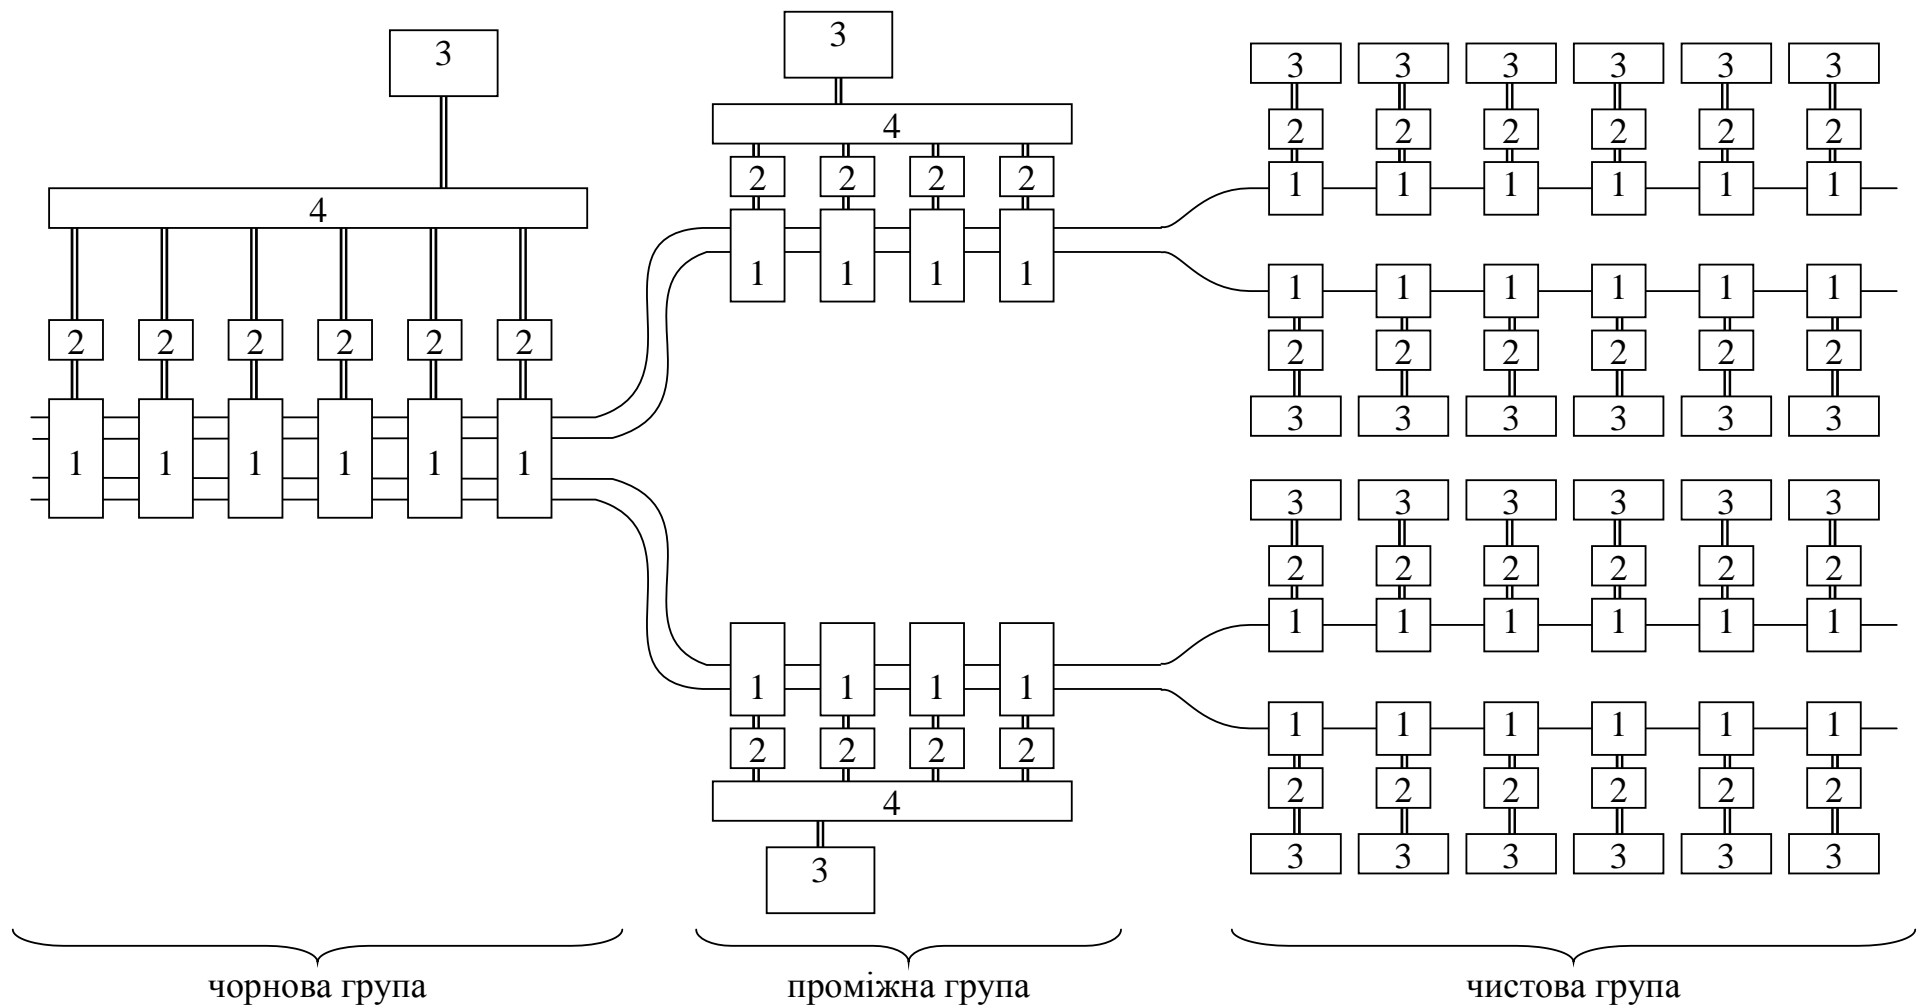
Схема розташування обладнання неперервного дротового стану
